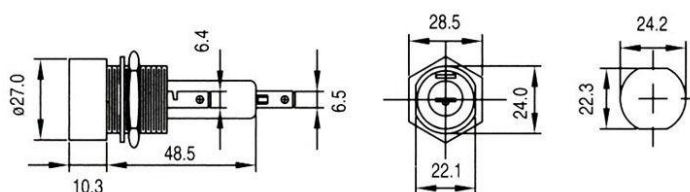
Габаритный чертеж держателя предохранителя CQ-225
